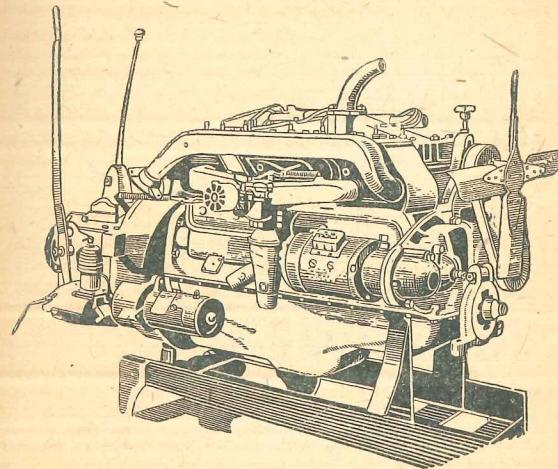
Двигатель ЗИС-21 (вид со стороны смесителя)
